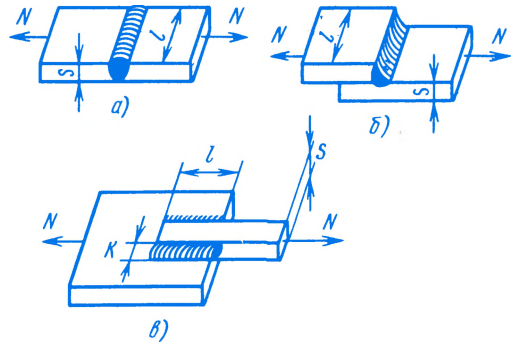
Определение расчетных усилий на сварные швы:
